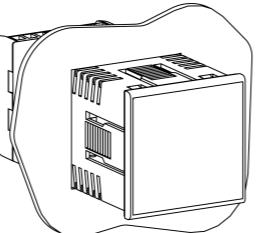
Монтаж прибора щитового крепления Щ5
